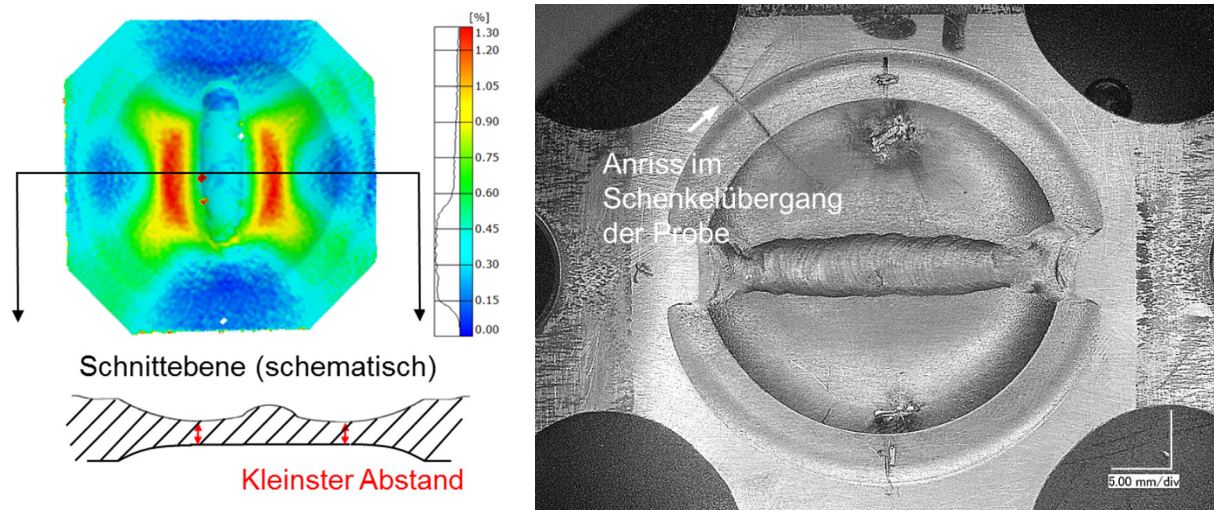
Versagensort geschweißter Kreuzproben mit unbearbeiteter Schweißnaht; Links: Hauptdehnungsfeld, Versagen am geringsten Querschnitt; Rechts: Versagen im Schenkelübergang
